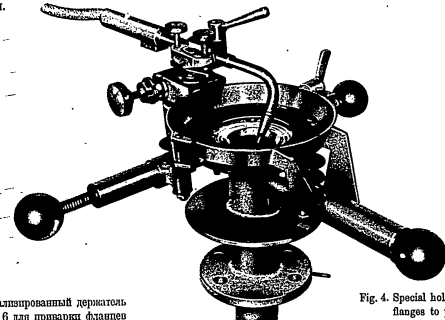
Специализированный держатель ДШ-16 для приварки фланцев к трубам
